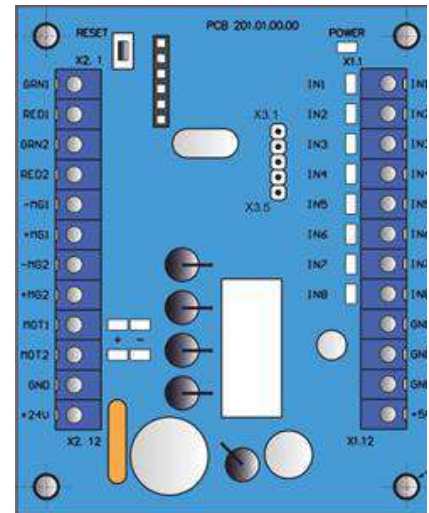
Зовнішній вигляд контролера моторизованого механізму PCB.201.01.00.00
